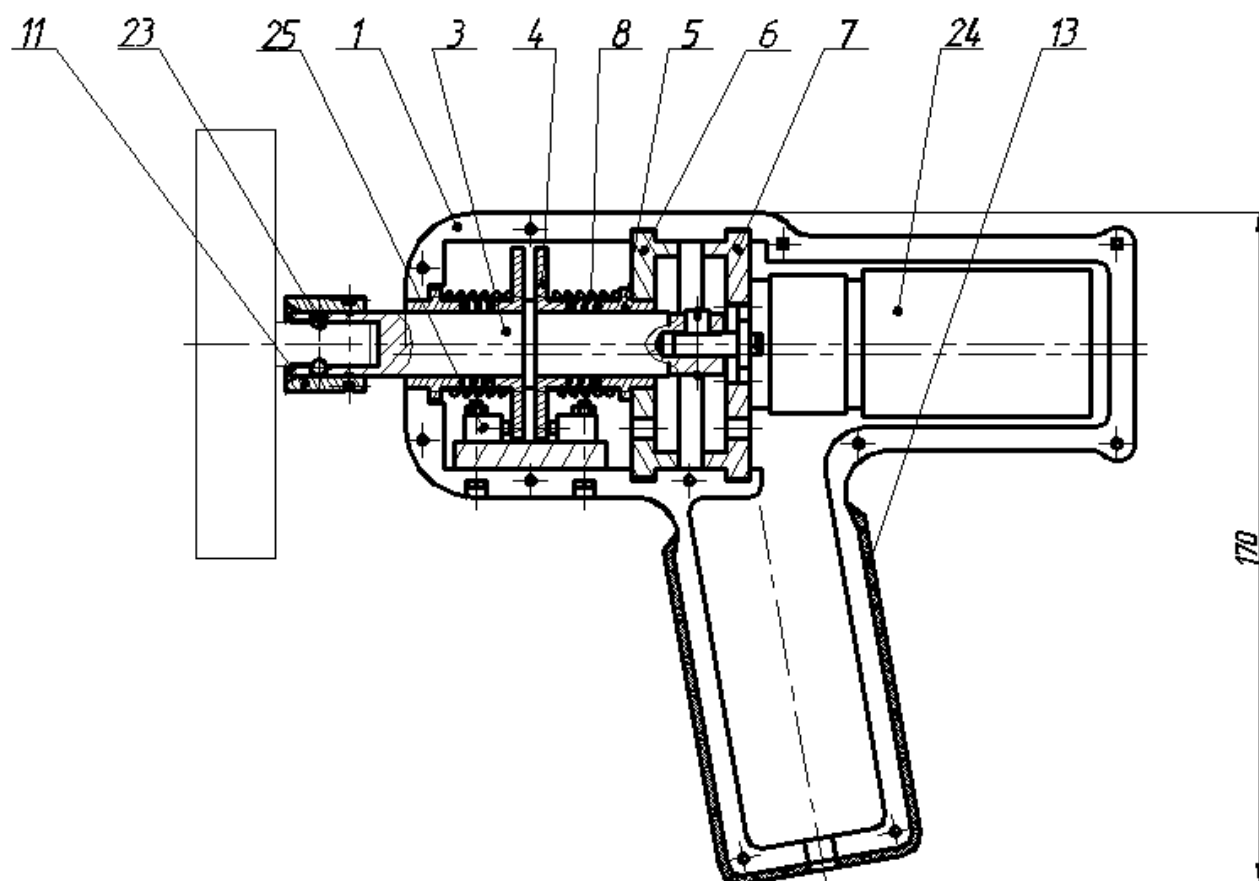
Приспособление для контроля внутренних резьб
